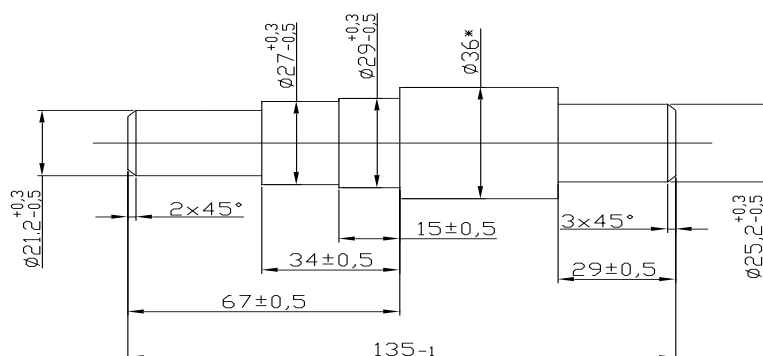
Чертеж поковки «Палец цилиндра»
